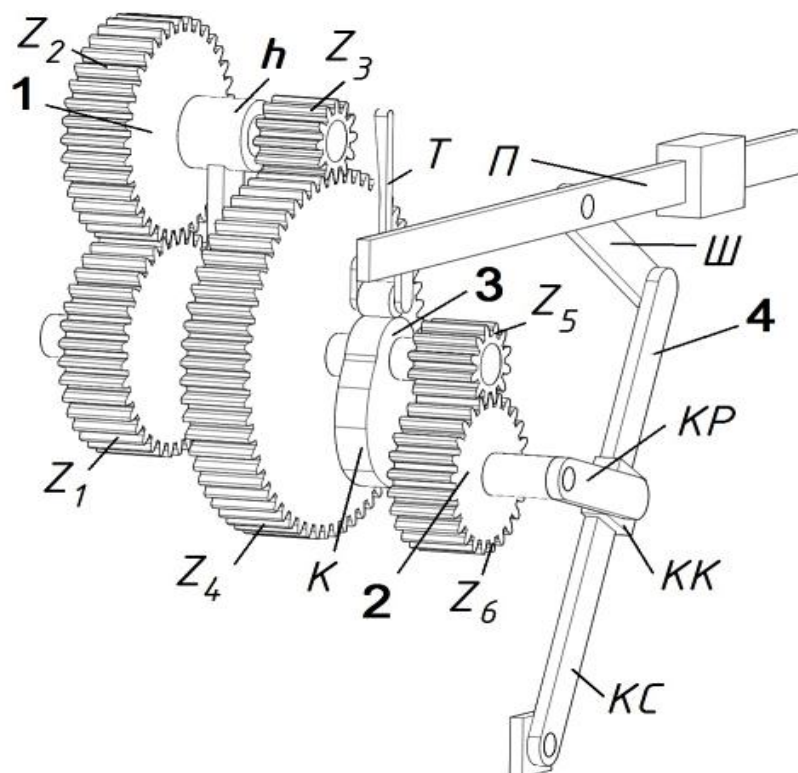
Механизм поперечно-строгального станка: 1 – планетарный зубчатый механизм; 2 – зубчатый ряд; 3 – кулачковый механизм; 4 – рычажный механизм; Z_1 – солнечное колесо; Z_2 , Z_3 – сателлиты; Z_4 – опорное колесо; h – водило; Z_5 , Z_6 – шестерня и колесо зубчатого ряда; K – кулачок; T – роликовый толкатель; KP – кривошип; $КС$ – кулиса; $КК$ – куличный камень; $Ш$ – шатун; $П$ – ползун.
